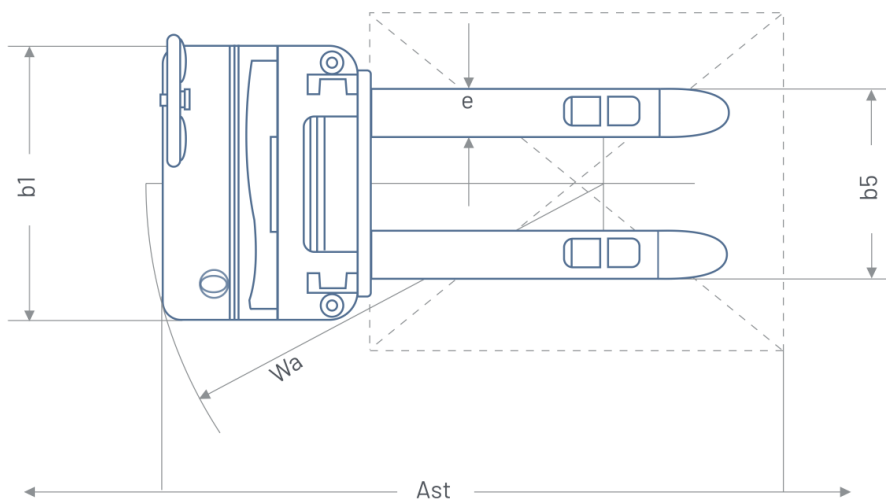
Draufsicht des DOUBLE-S mit Kürzeln
